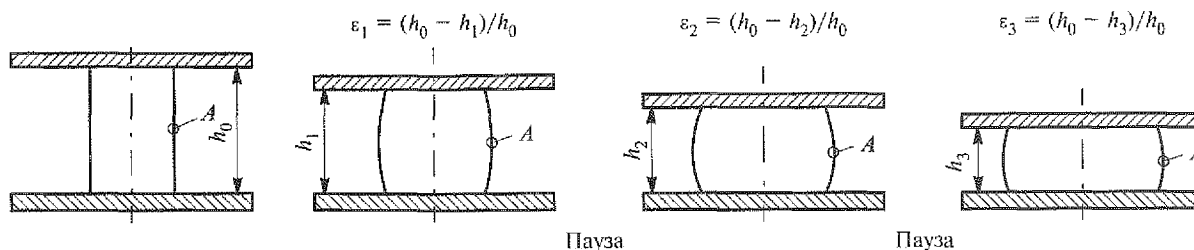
Схема осадки цилиндрической заготовки с промежуточными паузами
